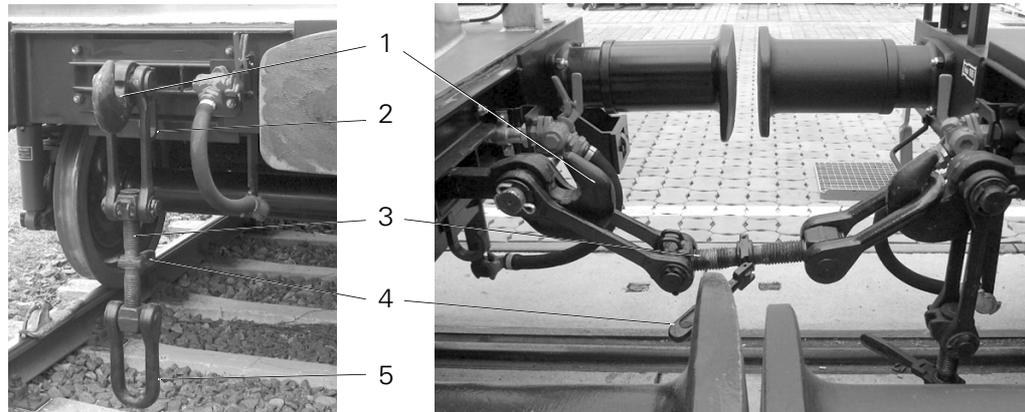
Zugvorrichtung - Schraubekupplung
